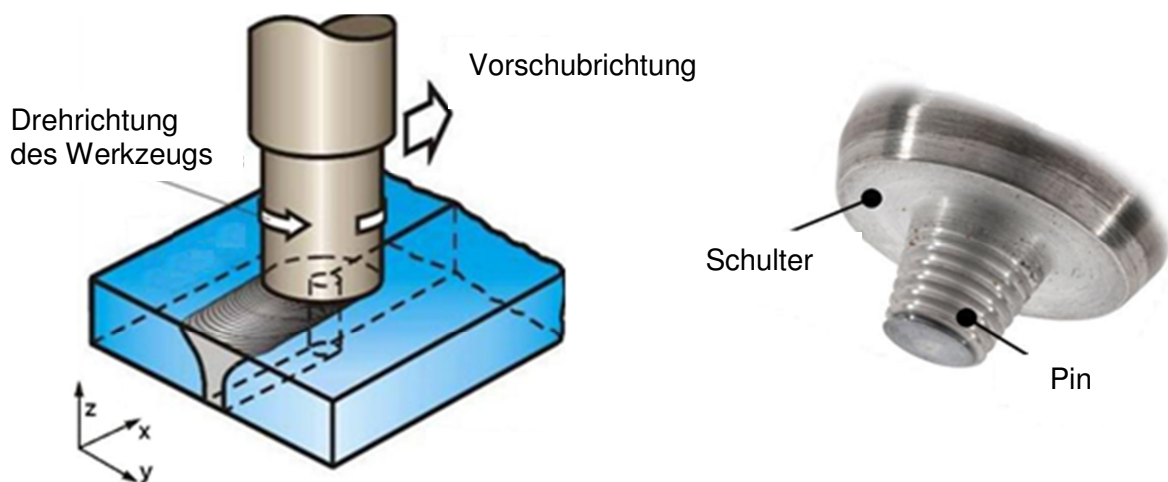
Prinzipskizze des FSW und Schweißwerkzeug /AiF09/
